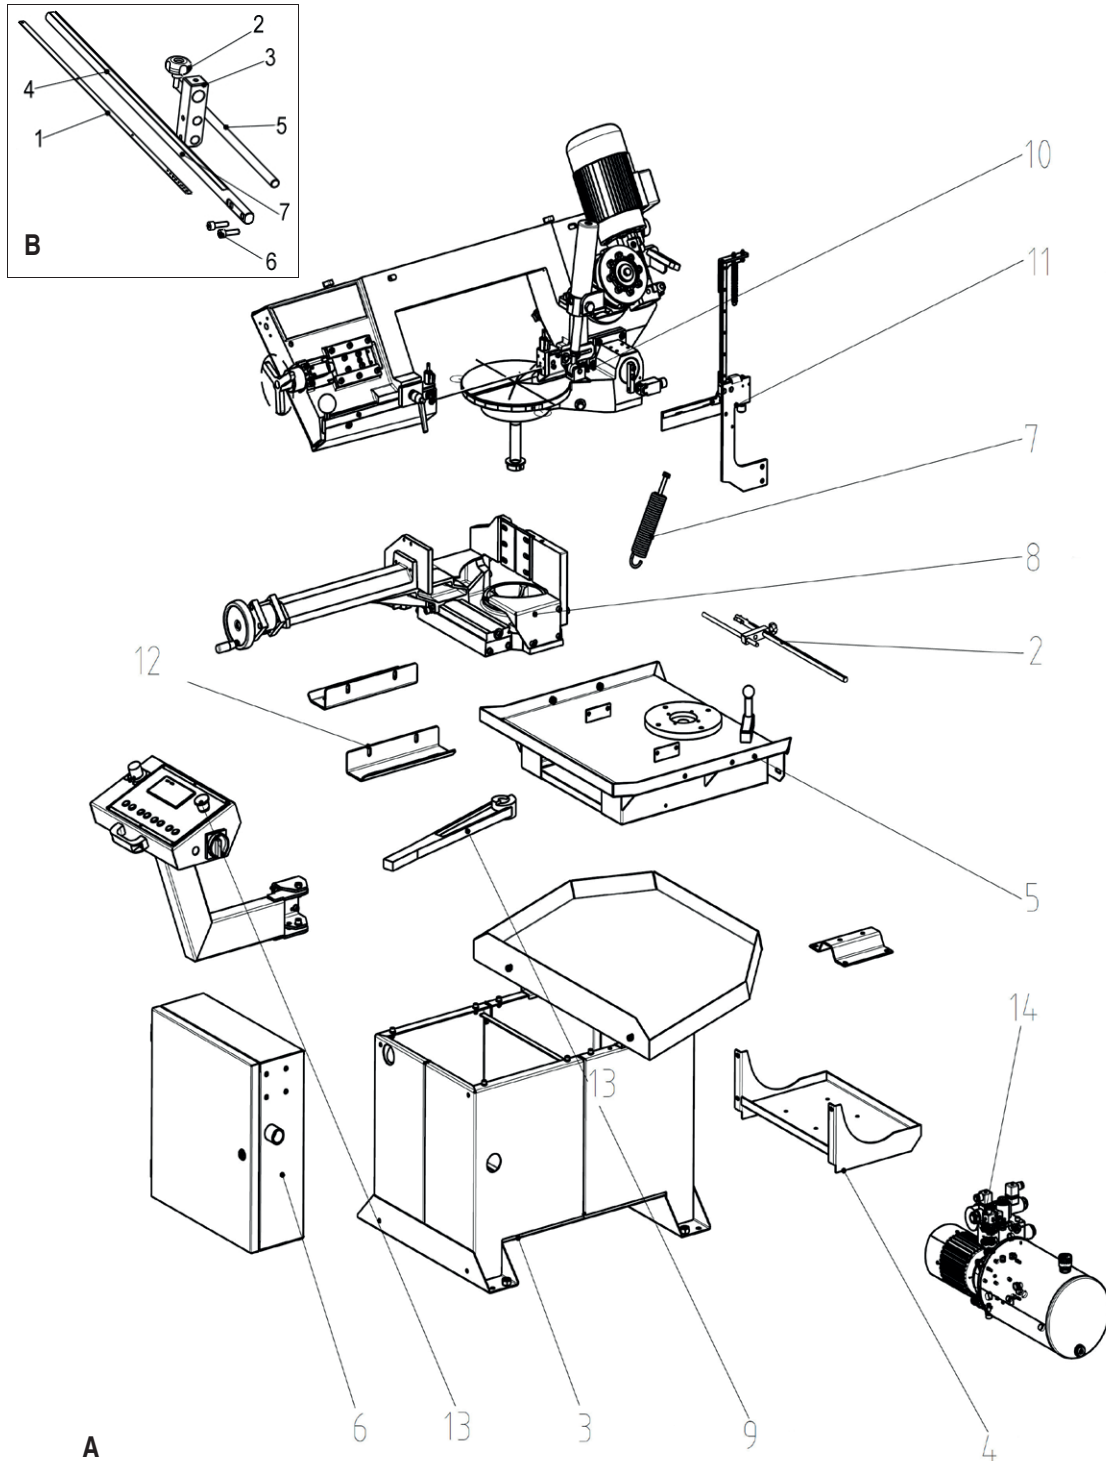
Dessin des pièces détachées 1 - A: Composants de la machine - B: Butée de longueur
